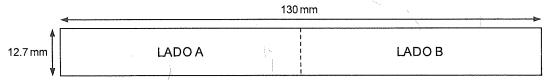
Dimensiones de la etiqueta para cables multipar.
